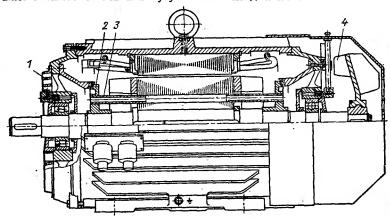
Асинхронный двигатель с короткозамкнутым ротором 4A280.
